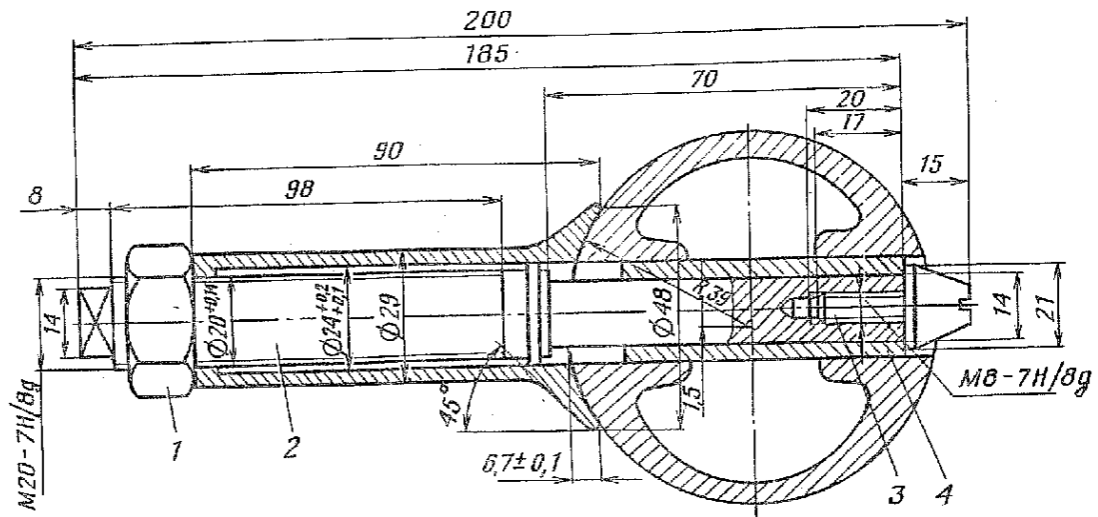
Приспособление для выпрессовки поршневого пальца:
